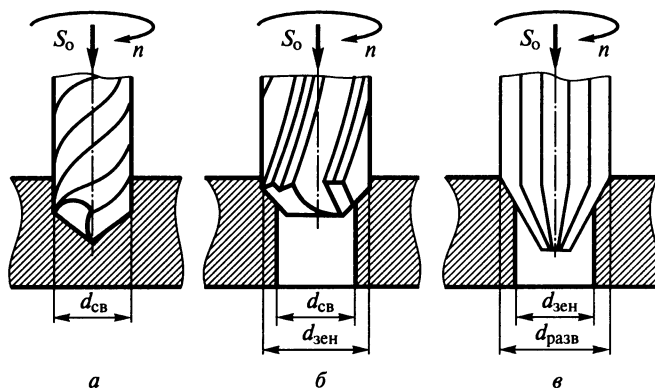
Схемы обработки деталей на сверлильном станке осевым инструментом: а — сверление; б — зенкерование; в — развертывание
